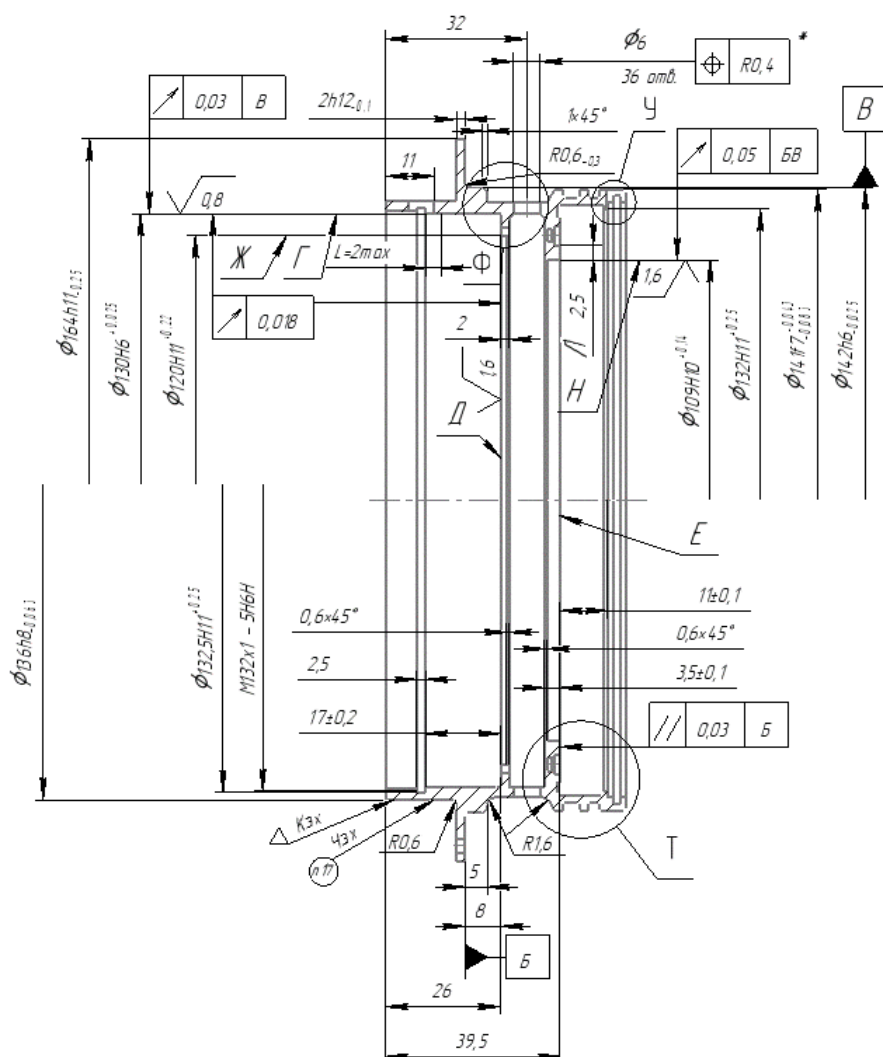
Чертеж детали «Корпус роликоподшипника».
